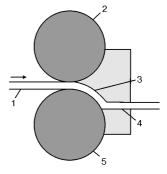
Схема установки комбинированной прокатки и равноканального углового прессования для получения длинномерных прутков: 1— образец, 2— направляющий валок, 3— зазор между валками, 4— выходной канал, 5— подающий валок
